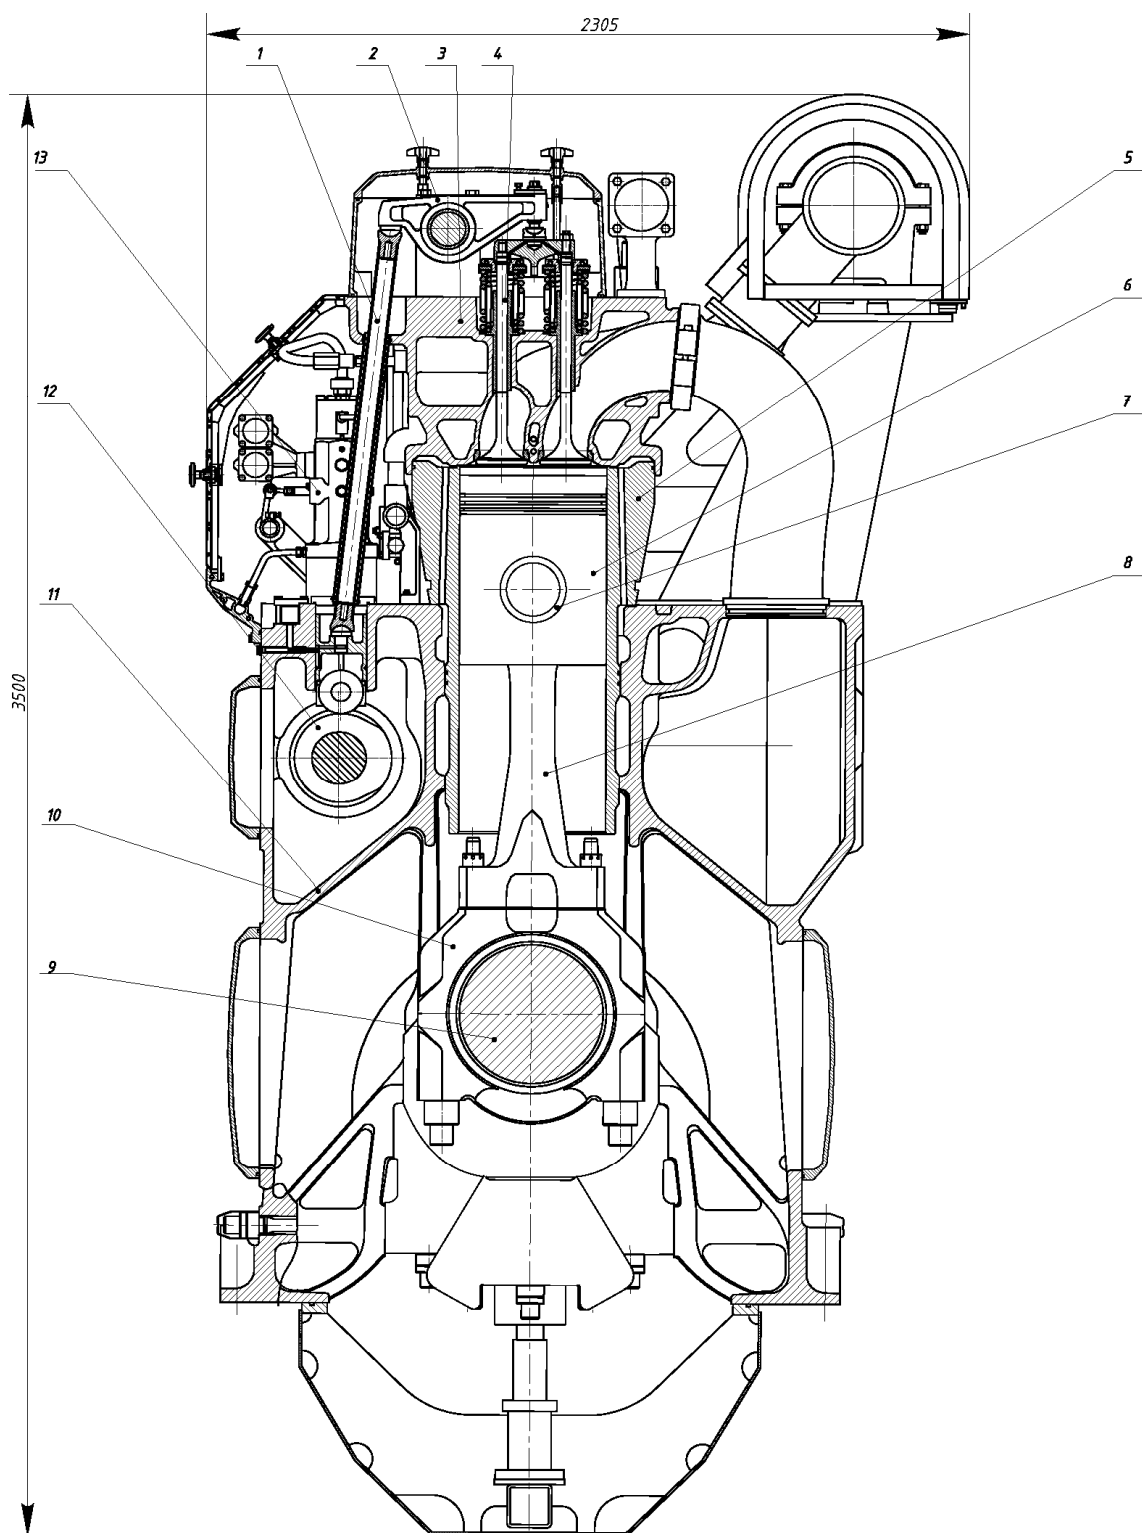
Загальний вигляд двигуна Wärtsilä L32C: 1 – штанга штовхача; 2 – коромисло приводу клапану; 3 – кришка циліндру; 4 – клапан; 5 – гільза циліндру; 6 – поршень; 7 – поршневий палець; 8 – стержень шатуна; 9 – колінчастий вал; 10 – нижня головка шатуна; 11 – картер двигуна; 12 – розподільний вал; 13 – ПНВТ
